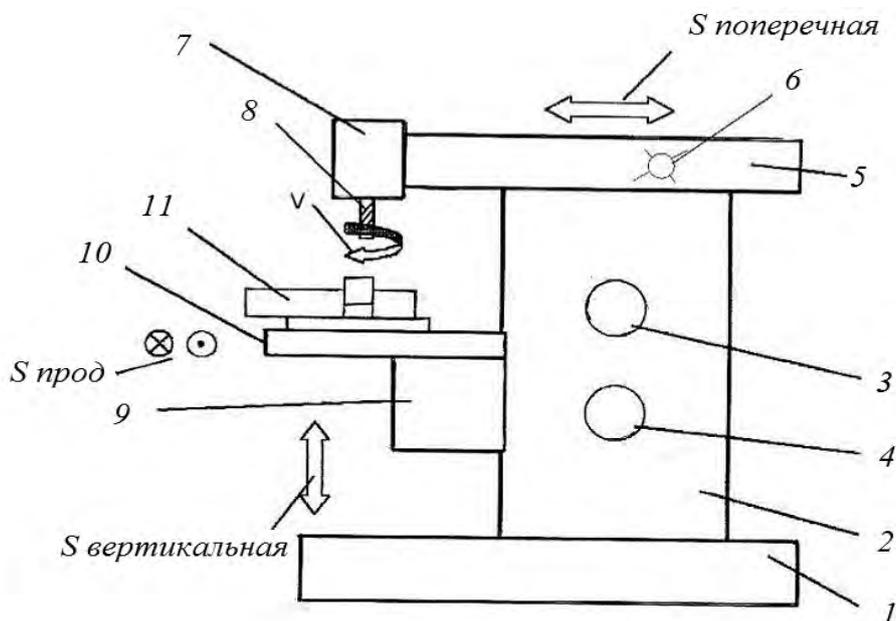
Общий вид фрезерного станка модели 676
